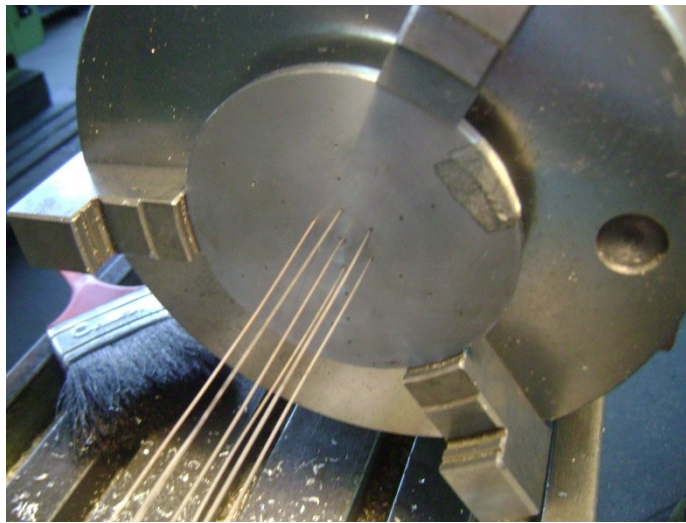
Disco II instalado en el rotor de la fresadora
